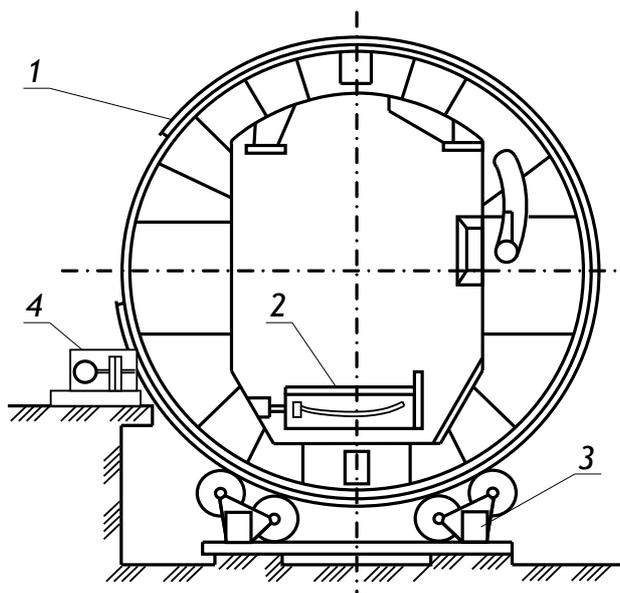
Роторный вагоноопрокидыватель с редукторным приводом:
